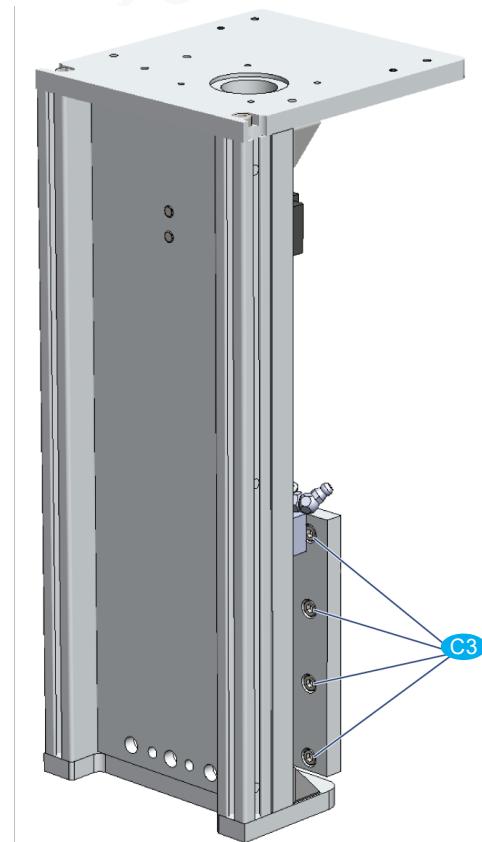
Verschraubung der Z-Achse an der Führungsplatte
